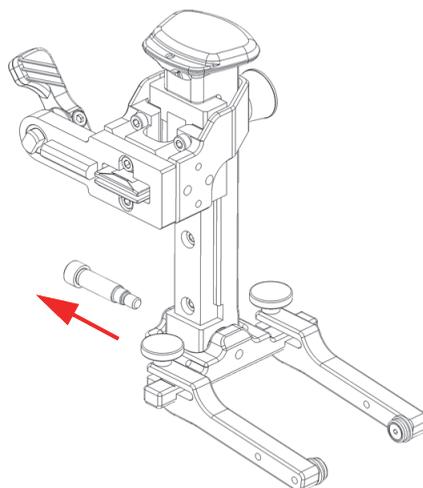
Schraube vom Schwenkträger des Gabelstücks entfernen
